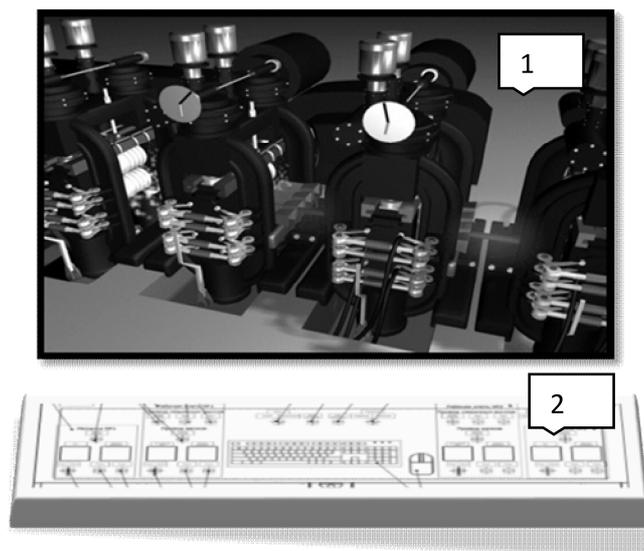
Внешний вид тренажера оператора прокатного стана:
